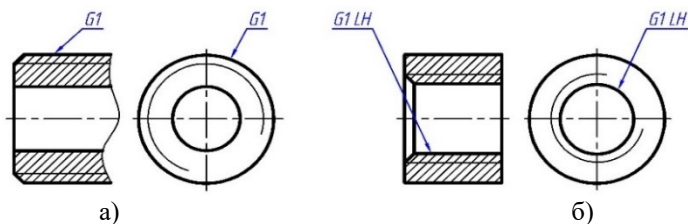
Позначення трубної циліндричної нарізі на кресленнику
